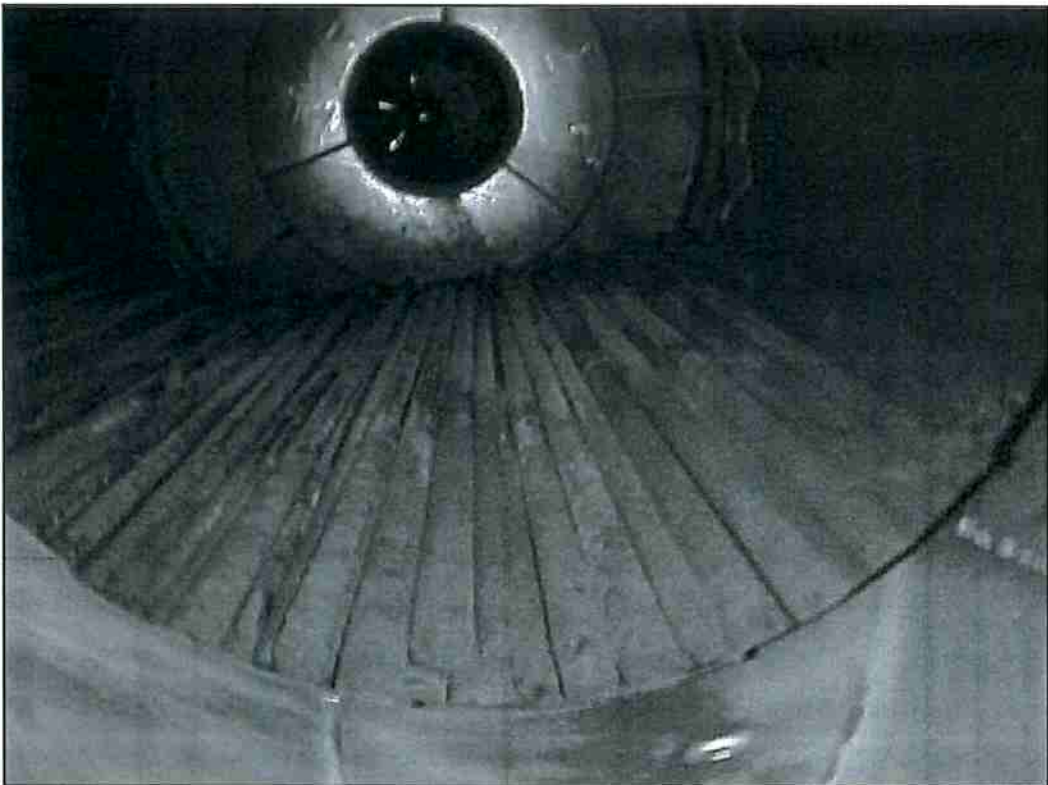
Foto interna da câmara de barras do moinho 025-MO-41
